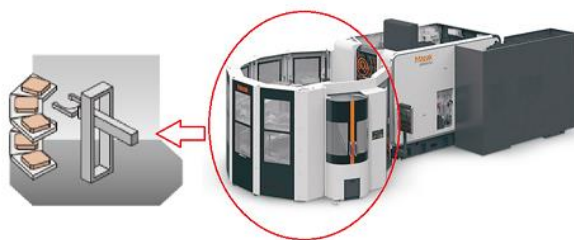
Zásobník nástrojů diskový s JÚ manipulátorem [34]
